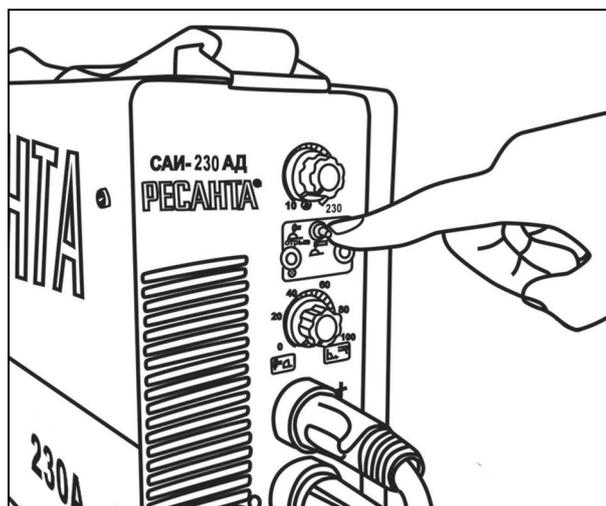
Установка тумблера для сварки в режиме TIG
